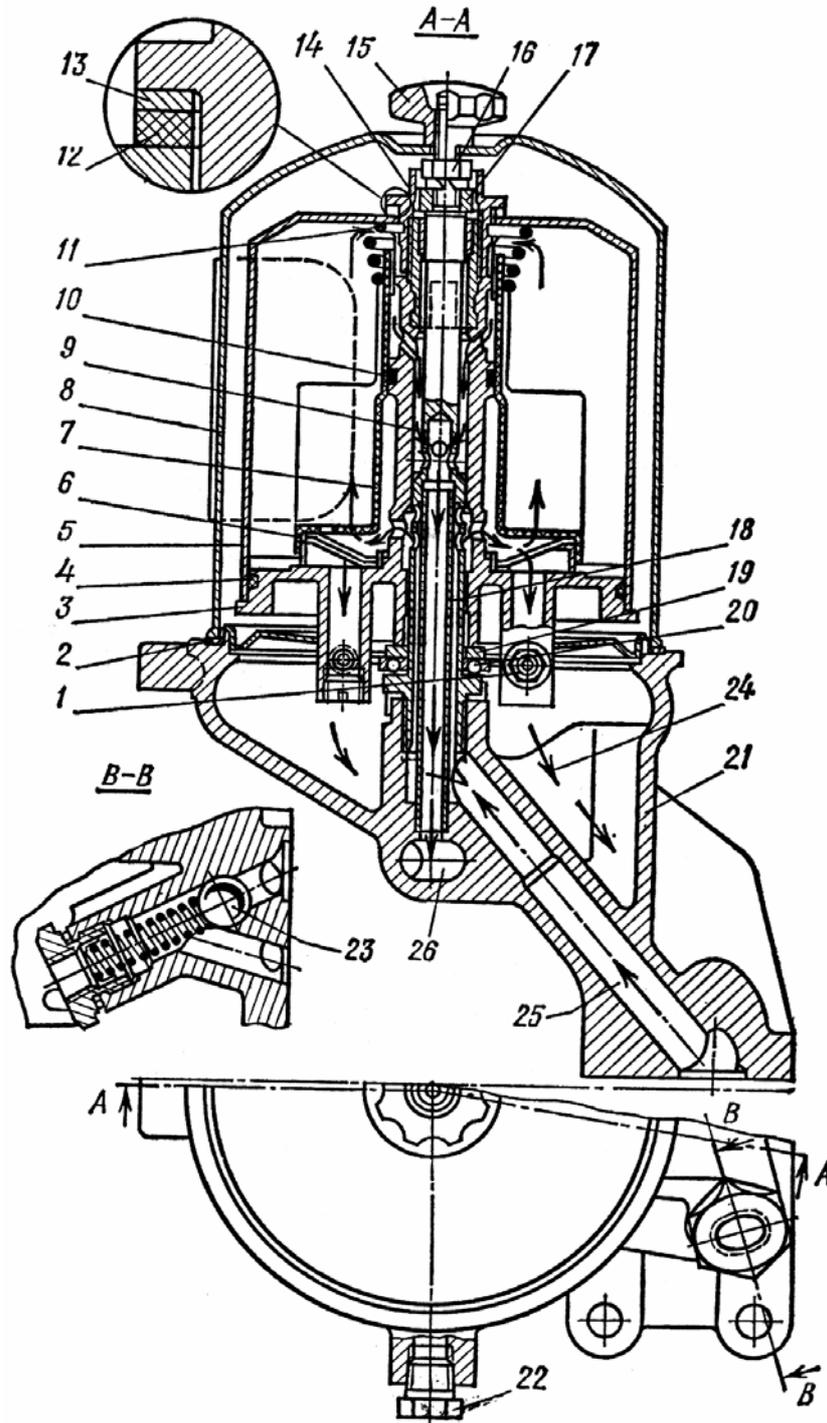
Фильтр центробежной очистки масла двигателя ЗИЛ-130:
